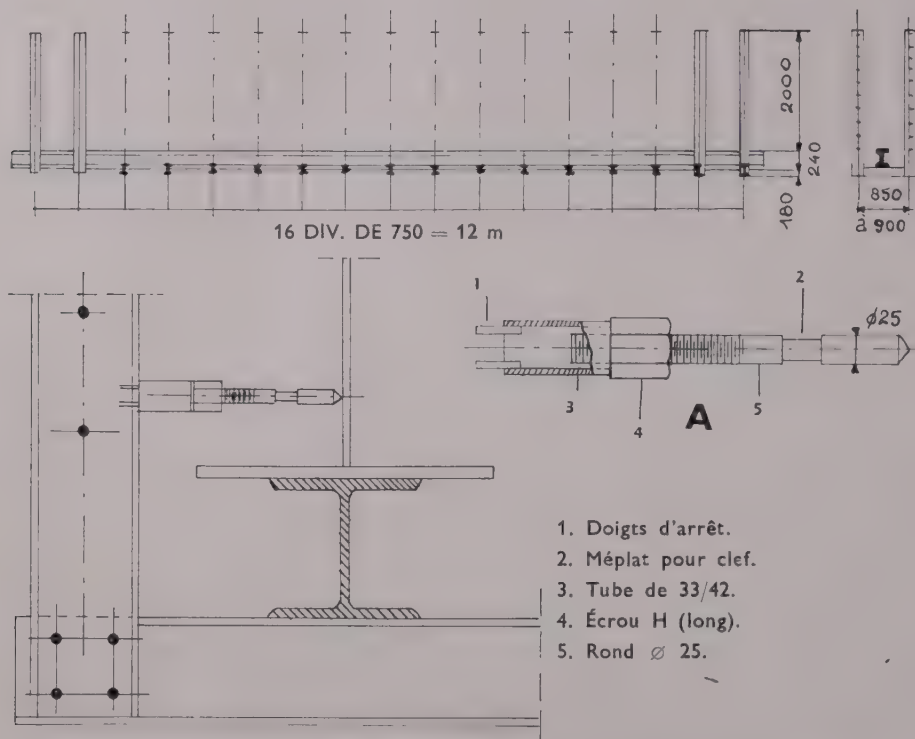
Dispositif de montage-pointage pour la construction de poutres soudées.
